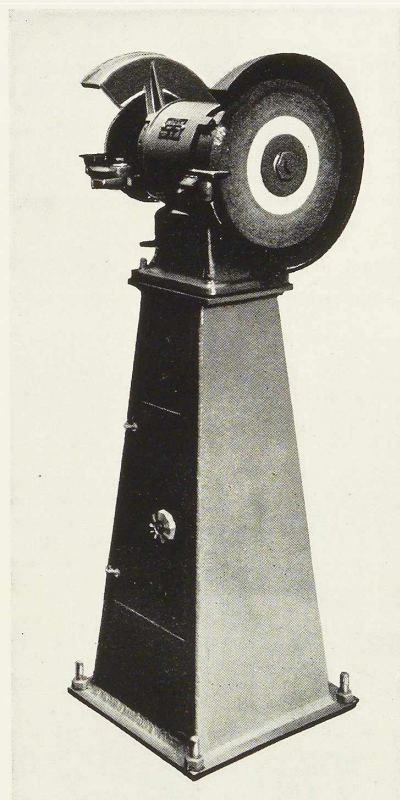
Bâti de meule en tôle d'acier découpée et assemblée par soudure oxy-acétylénique.
